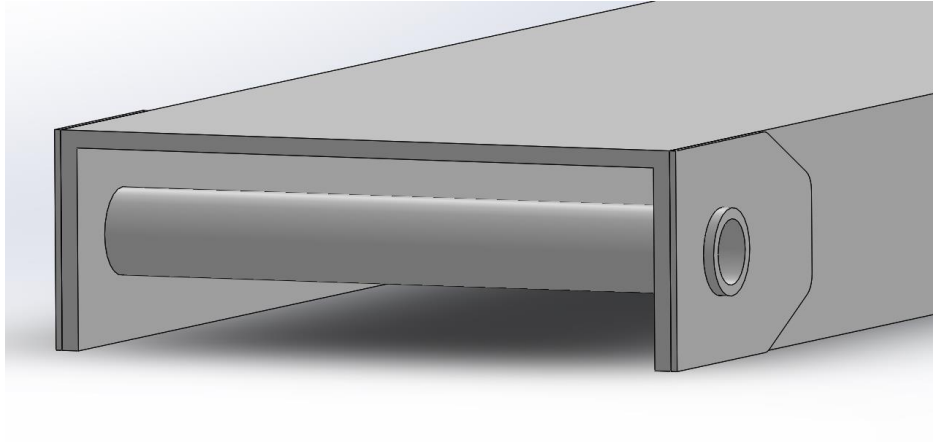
Resultado chapa soldada y casquillo dimensionado
